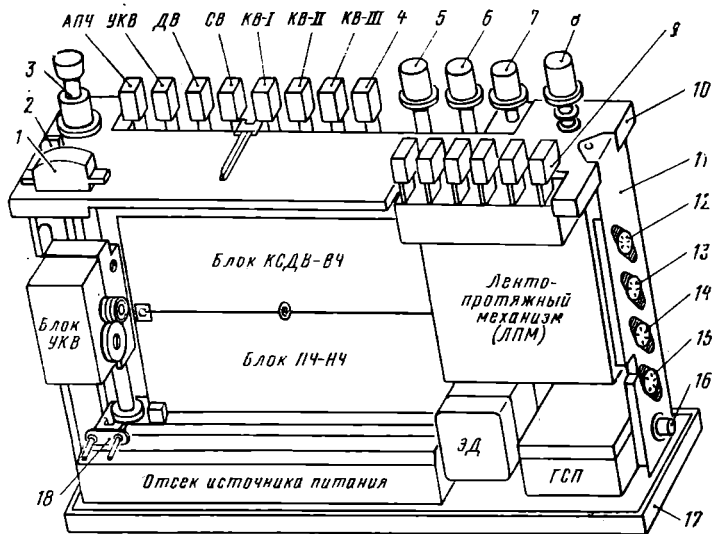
Схема расположения основных узлов и деталей на шасси магнитолы «Ореанда-301»:
